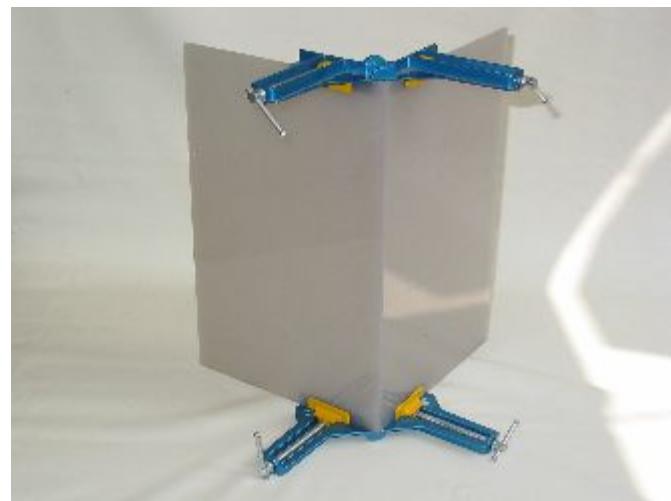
Die Gehäuse-Seitenteile werden beim Kleben mit Schraubzwingen fixiert
